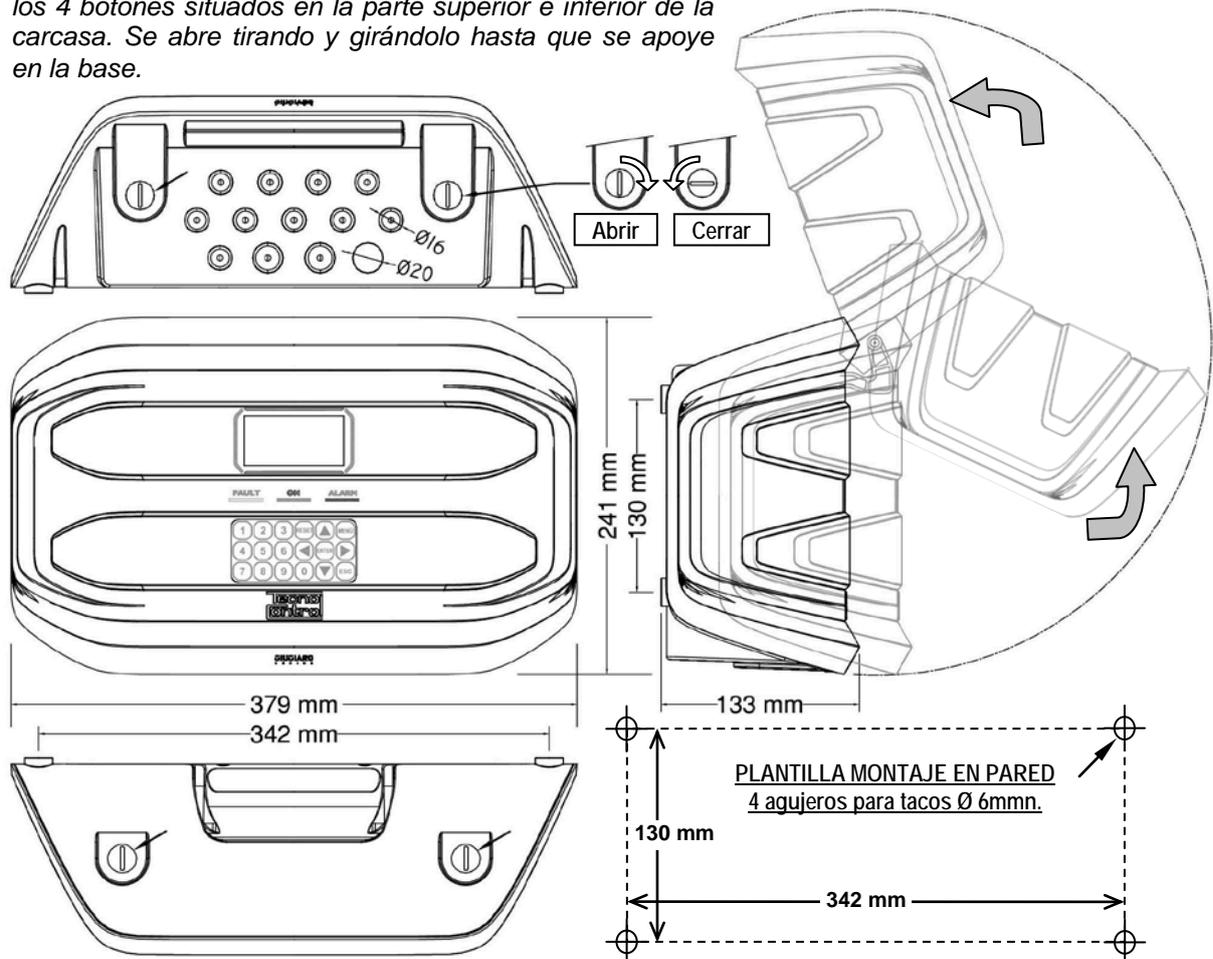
AE/GI-CE408PD Dimensiones y plantilla de montaje en pared
